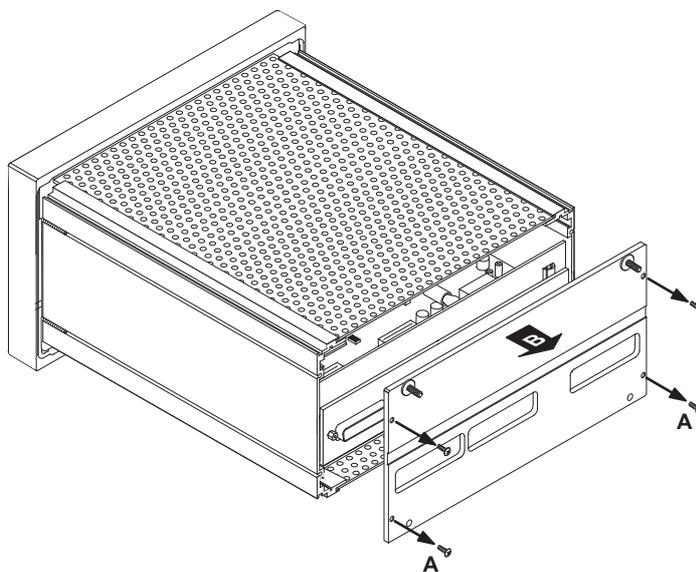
Entfernen der Abdeckung auf der Rückseite
